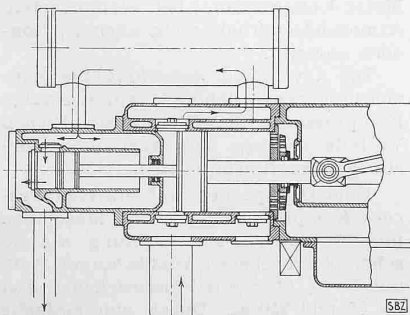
Kompressor eines zweistufigen Flugkolben-Kompressors für 35 at
